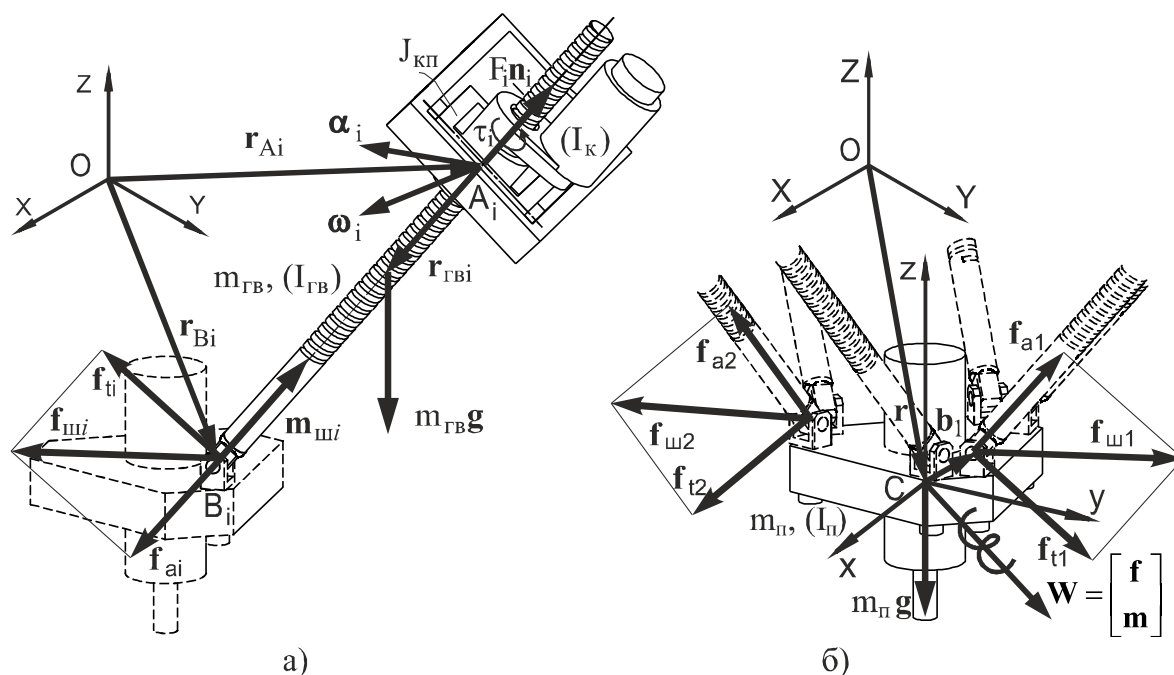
Розрахункові схеми: а) штанги змінної довжини; б) рухомої платформи
